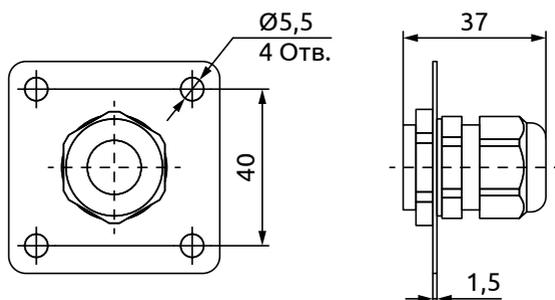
Габаритные размеры консоли HTE-HoldC
